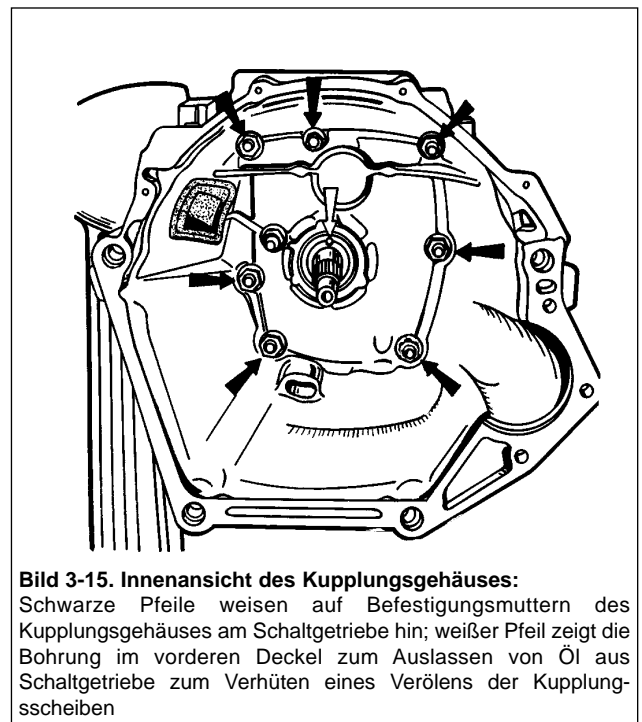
Innenansicht des Kupplungsgehäuses:
